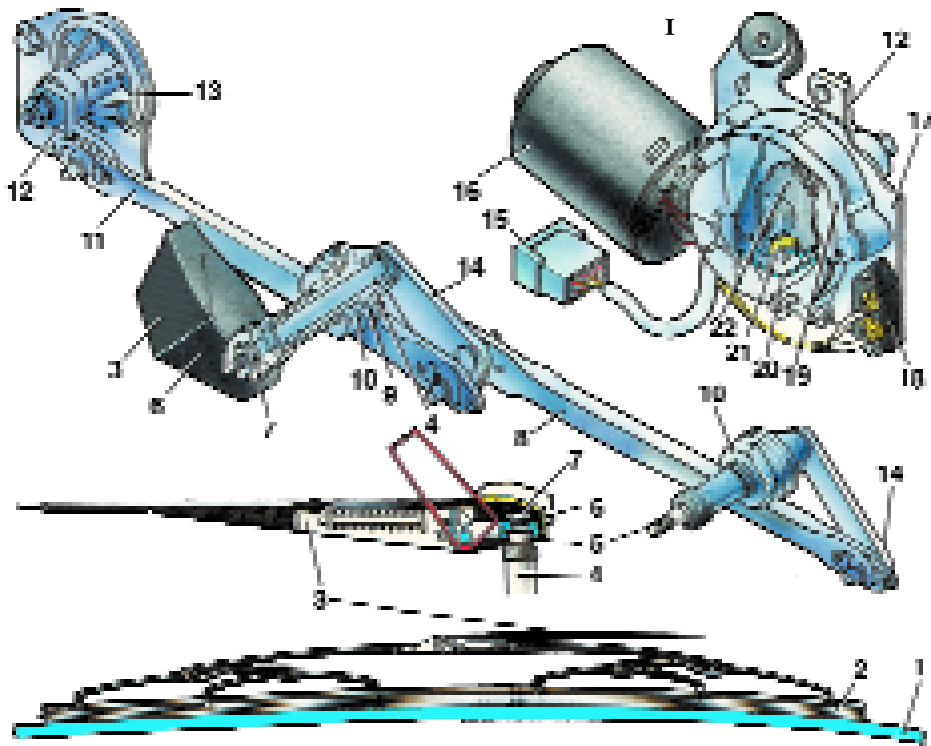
Стеклоочиститель 31.5205-02: 1 – ветровое стекло; 2 – щетка; 3 – рычаг; 4 – установочная втулка; 5 – вал; 6 – колпачок рычага; 7 – гайка крепления рычага; 8 – большая тяга; 9 – подкладка; 10 – гайка втулки; 11 – малая тяга; 12 – кривошип; 13 – редуктор; 14 – поводок; 15 – штекерная колодка; 16 – электродвигатель; 17 – кронштейн; 18 – предохранитель; 19 – панель; 20 – крышка; 21 – контакты; 22 – шестерня редуктора; I – моторредуктор
